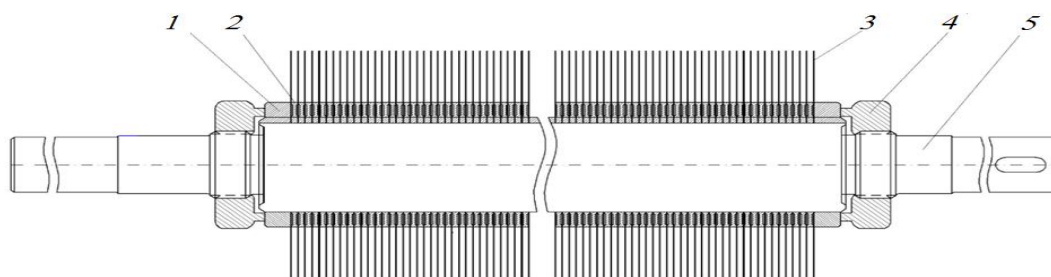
Пильный цилиндр пильного джина марки 4ДП-130
